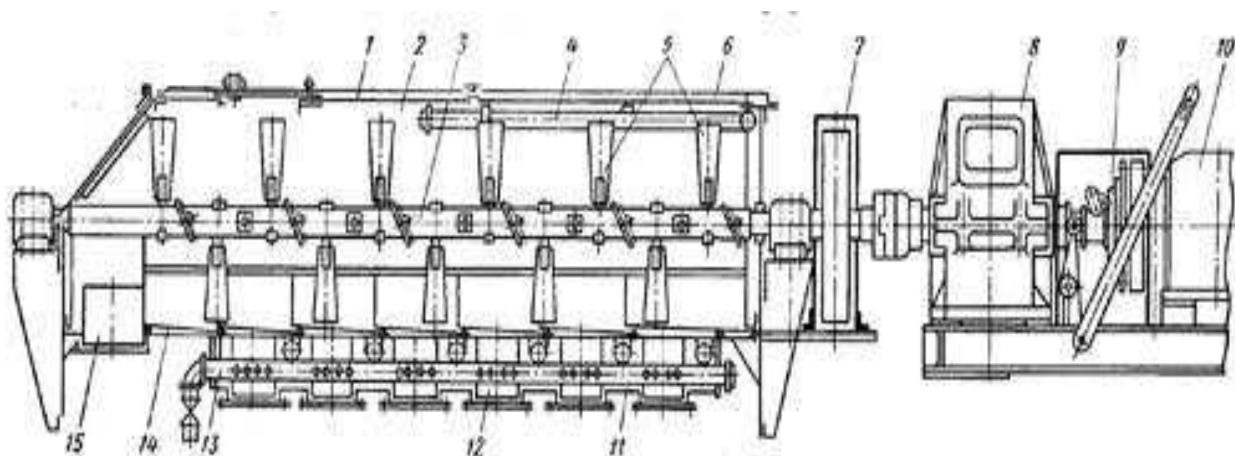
Двухвальный лопастной смеситель непрерывного действия
